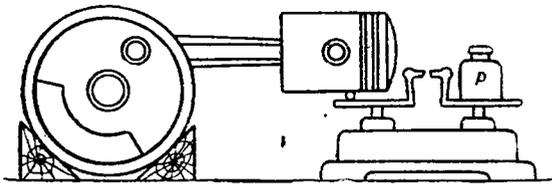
Способ взвешивания поршня и верхней части шатуна в сборе.
